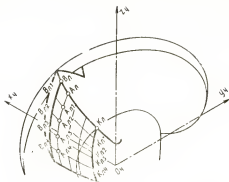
Сеть координатных линий на боковой затылованной поверхности червячной фрезы
